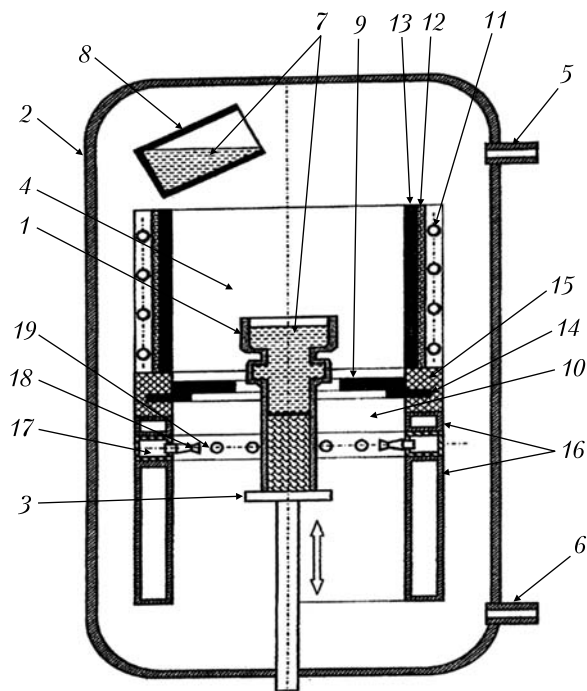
Схема модернізованого ливарного процесу для отримання виливків лопаток газових турбін з регулярною структурою: 1 – ливарна форма; 2 – вакуумний кожух; 3 – кристалізатор; 4 – зона нагрівання; 5 – труба для кріплення до вакуумної установки; 6 – труба для додаткового розвантаження зони охолодження робочої камери; 7 – розплав; 8 – тигель; 9 – теплоізоляційний екран; 10 – зона охолодження; 11 – індуктори зони нагрівання; 12 – теплоізоляція; 13 – графітова муфельна піч; 14 – стопорне кільце; 15 – циліндрична стінка теплоізоляційного екрана; 16 – кожух; 17 – кільцевий газозбірник; 18 – газові інжектори; 19 – отвори для газових інжекторів
